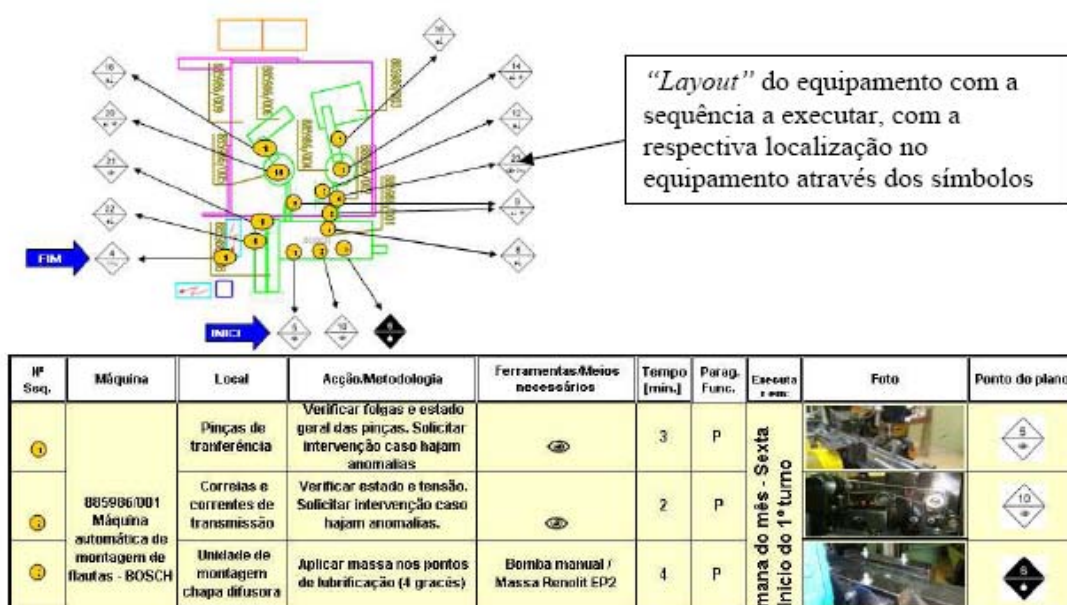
Plano de Manutenção autónoma utilizado noutra secção
